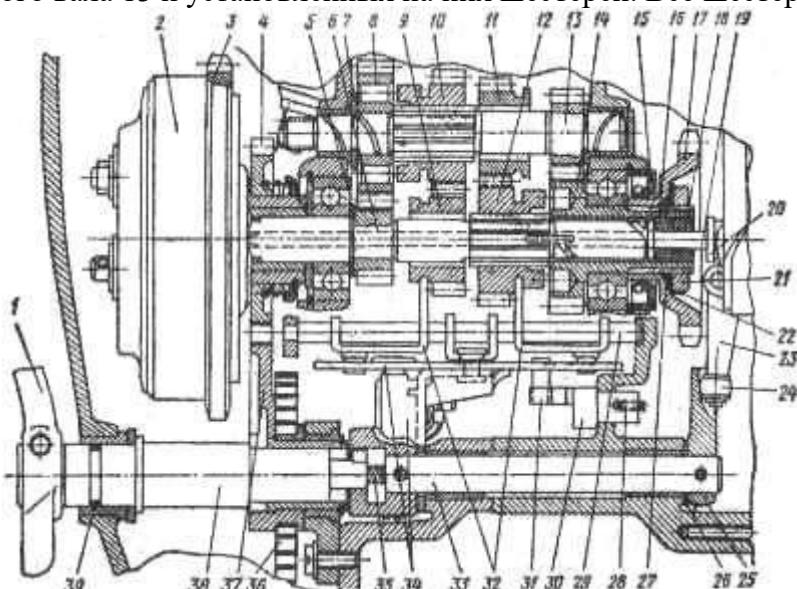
Разрез коробки передач, механизма переключения передач и пускового механизма:
